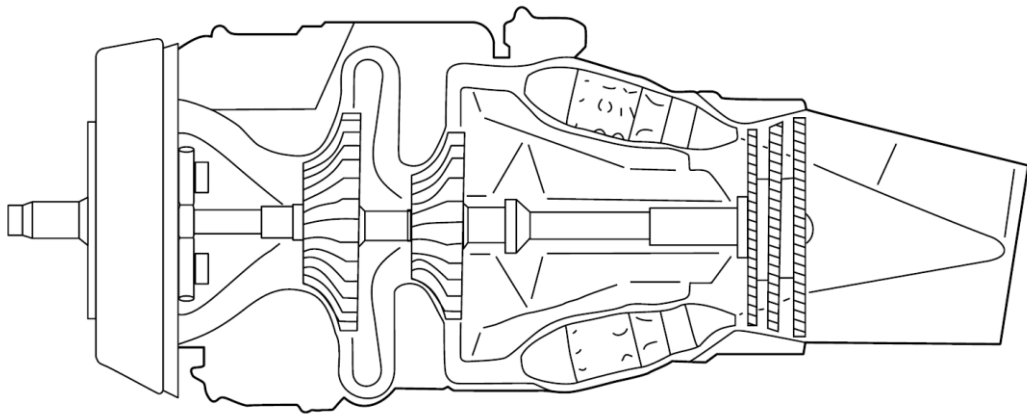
Motor turbo-hélice com turbina que aciona tanto o compressor como a hélice [4].
